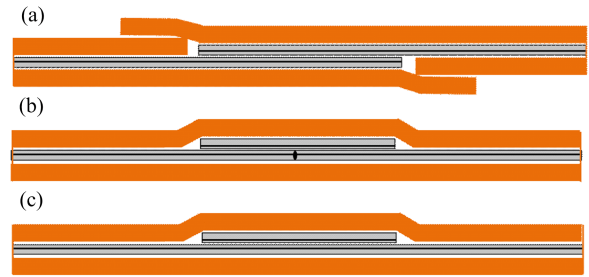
焊接头结构示意图:(a)2#-焊接头;
